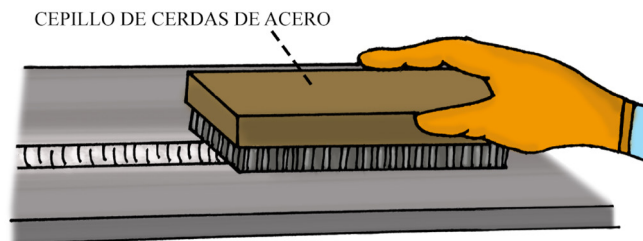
Limpieza final de cordón de soldadura.
